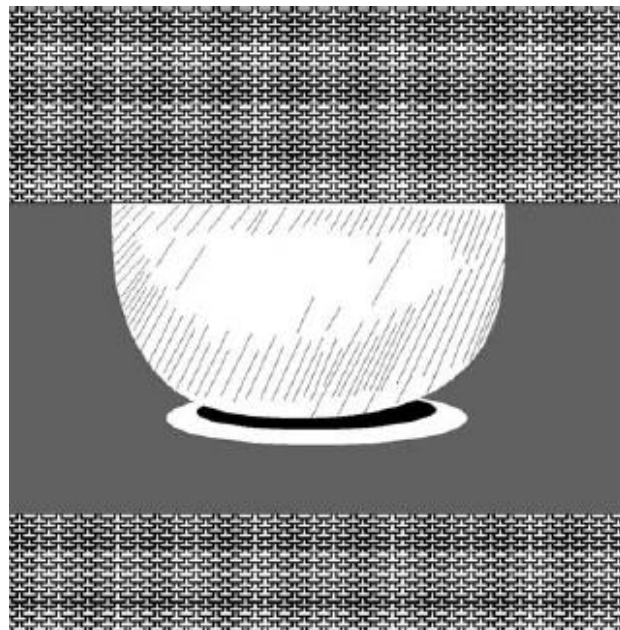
Unión de soldadura de un BGA mostrando una apertura [2].
